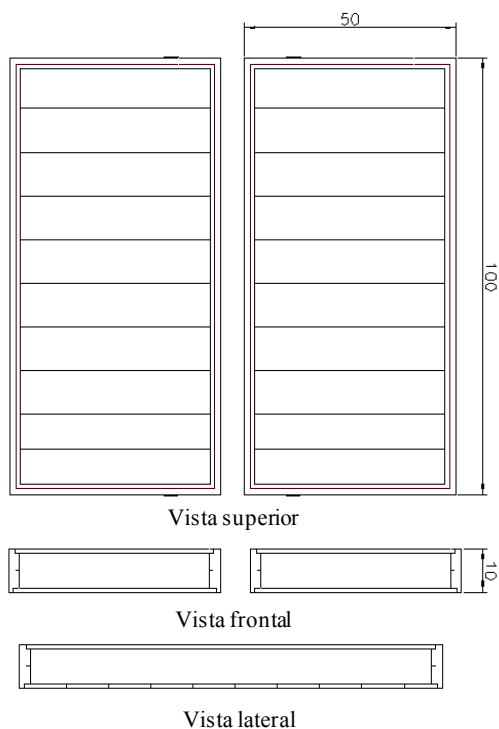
esquema (dimensões em cm) de construção da base em madeira para as placas
